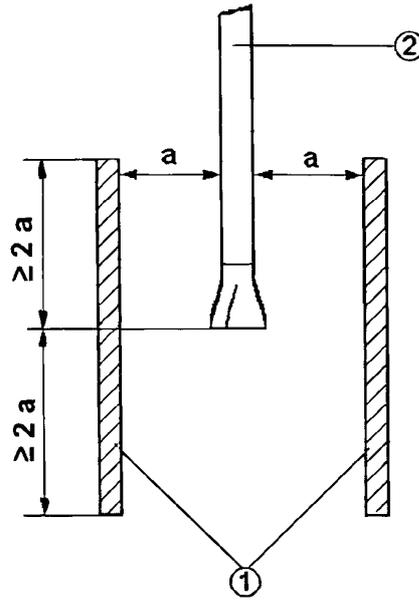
Mit einer U-förmigen Schutzeinrichtung ausgerüstete Gehrungskappsäge
